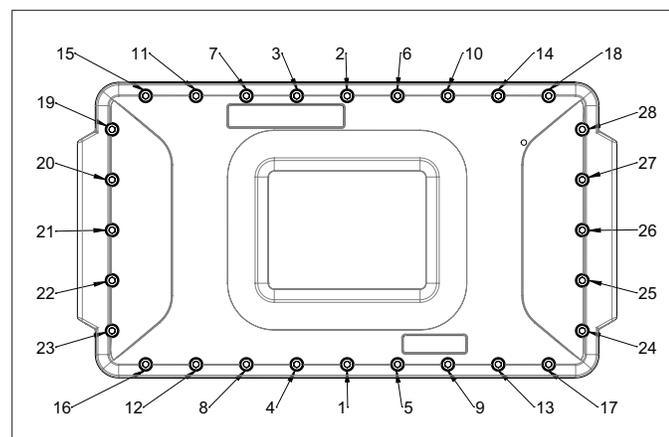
Schéma de couple de serrage des vis du couvercle pour l'AccuLoad IV-QT
